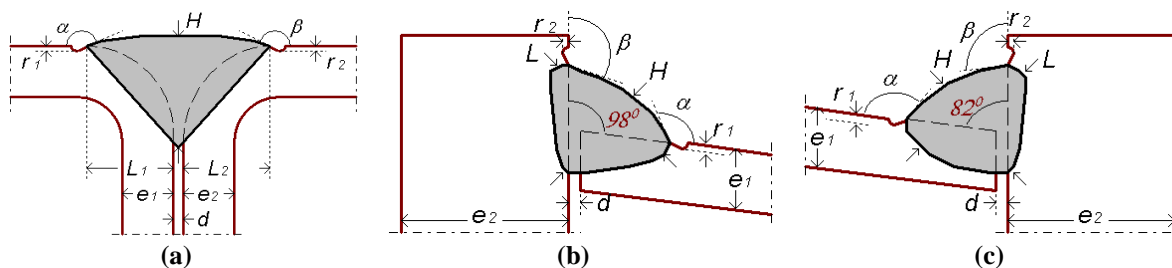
Especificações dimensionais das juntas soldadas: JR em (a), JCI em (b) e JCE em (c).
